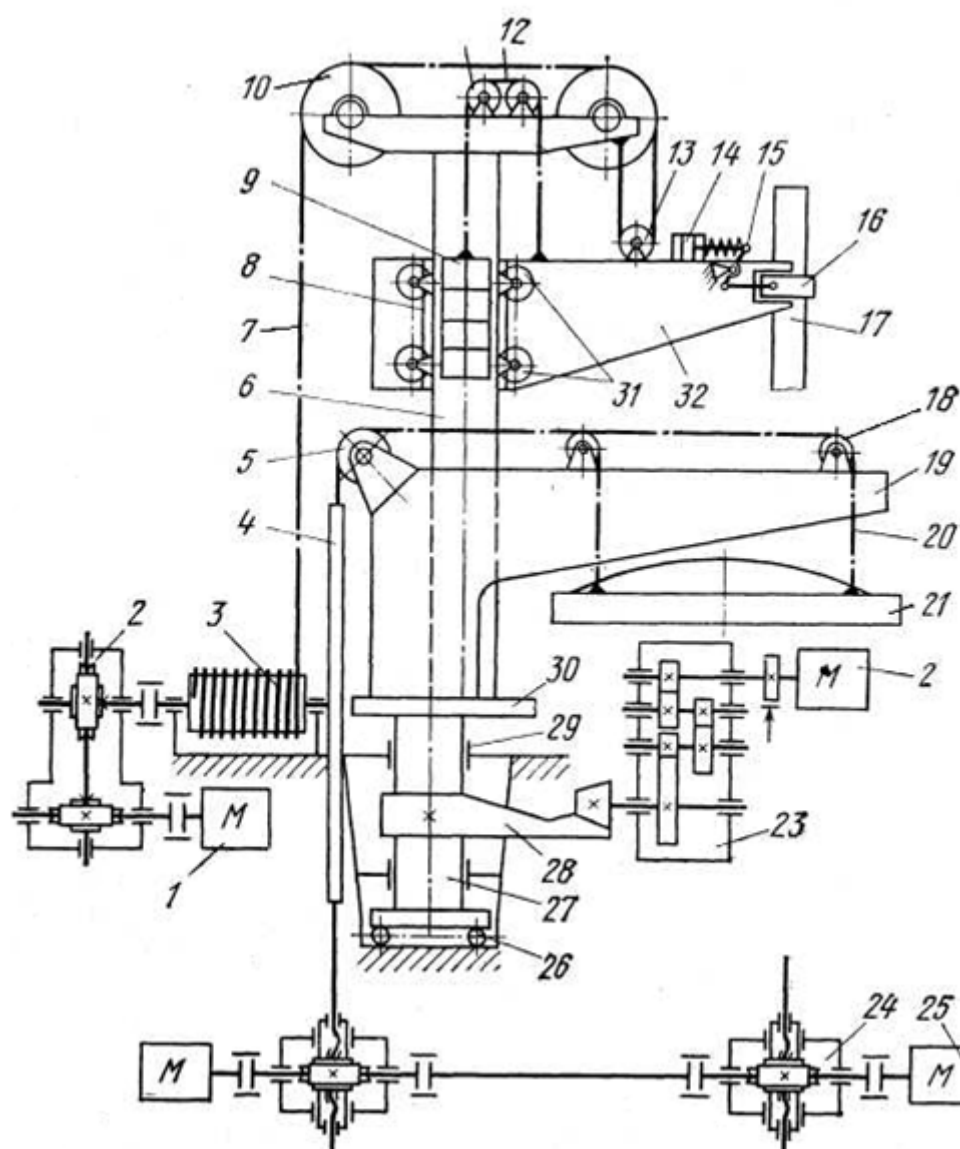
Кінематична схема механізму повороту склепіння
